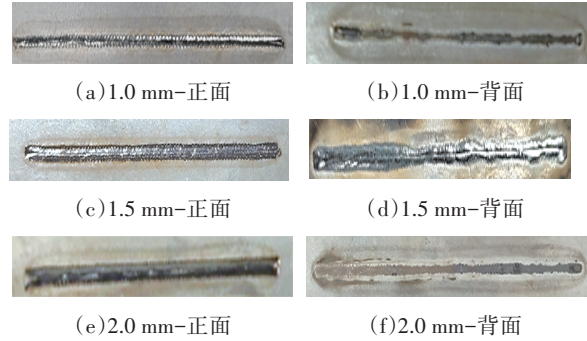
不同焊接摆幅下表面与背部的焊缝形貌
